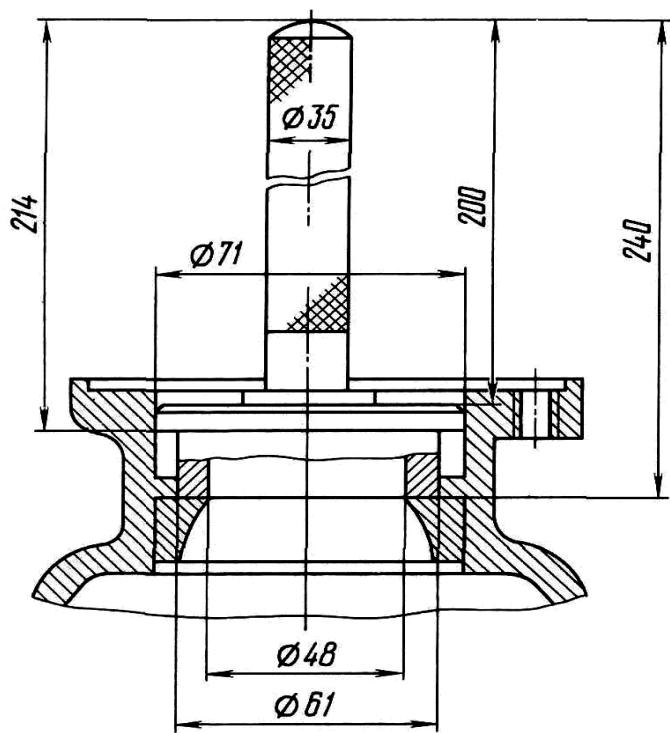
Выпрессовка наружной обоймы сферического подшипника
